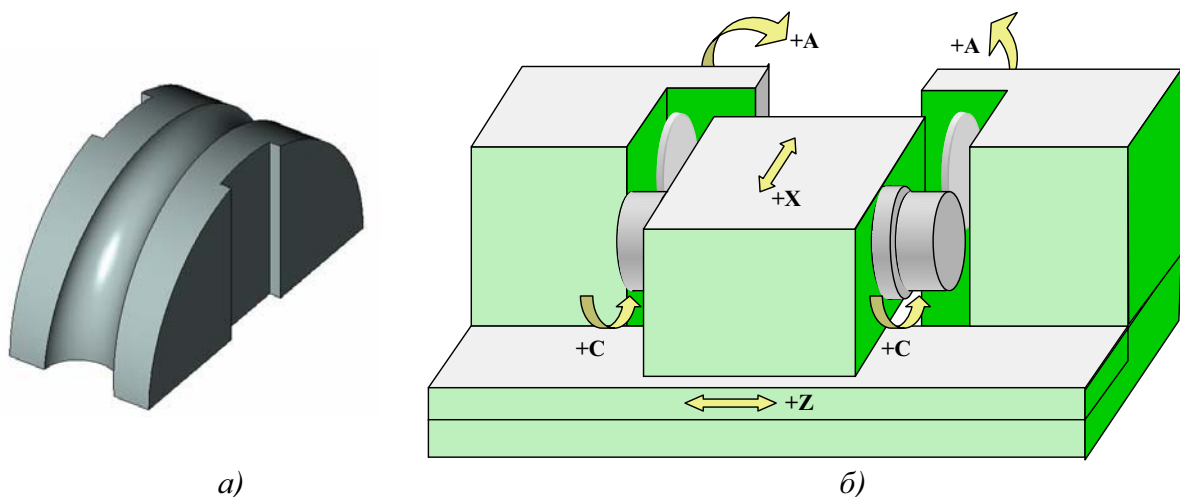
Калибр пильгерования труб (а) и схема станка для его изготовления (б)
